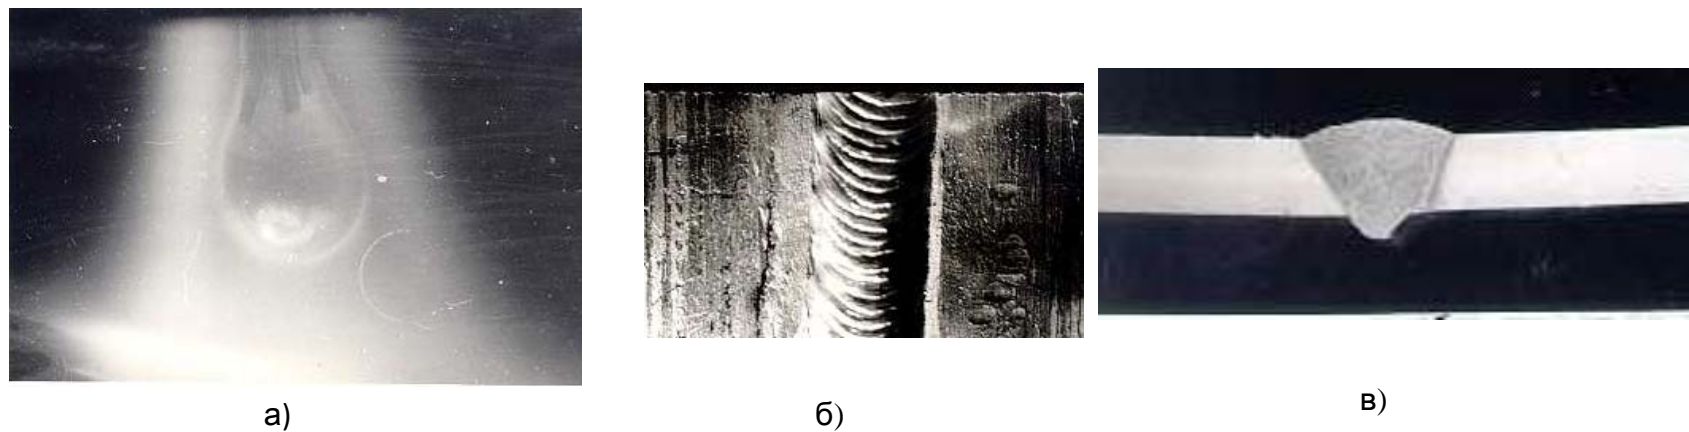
Плазменная сварка плавящимся электродом обесточенной проволокой, сплав АМг6, $\delta=6\text{мм}$. а) внешний вид процесса; б) внешний вид сварного шва; в) макрошлиф.
